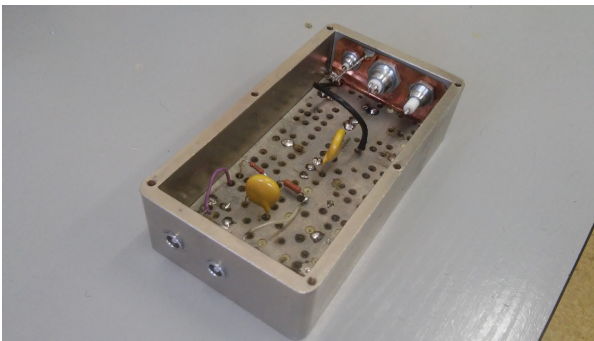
Часть сборки без кремниевого фотоумножителя
